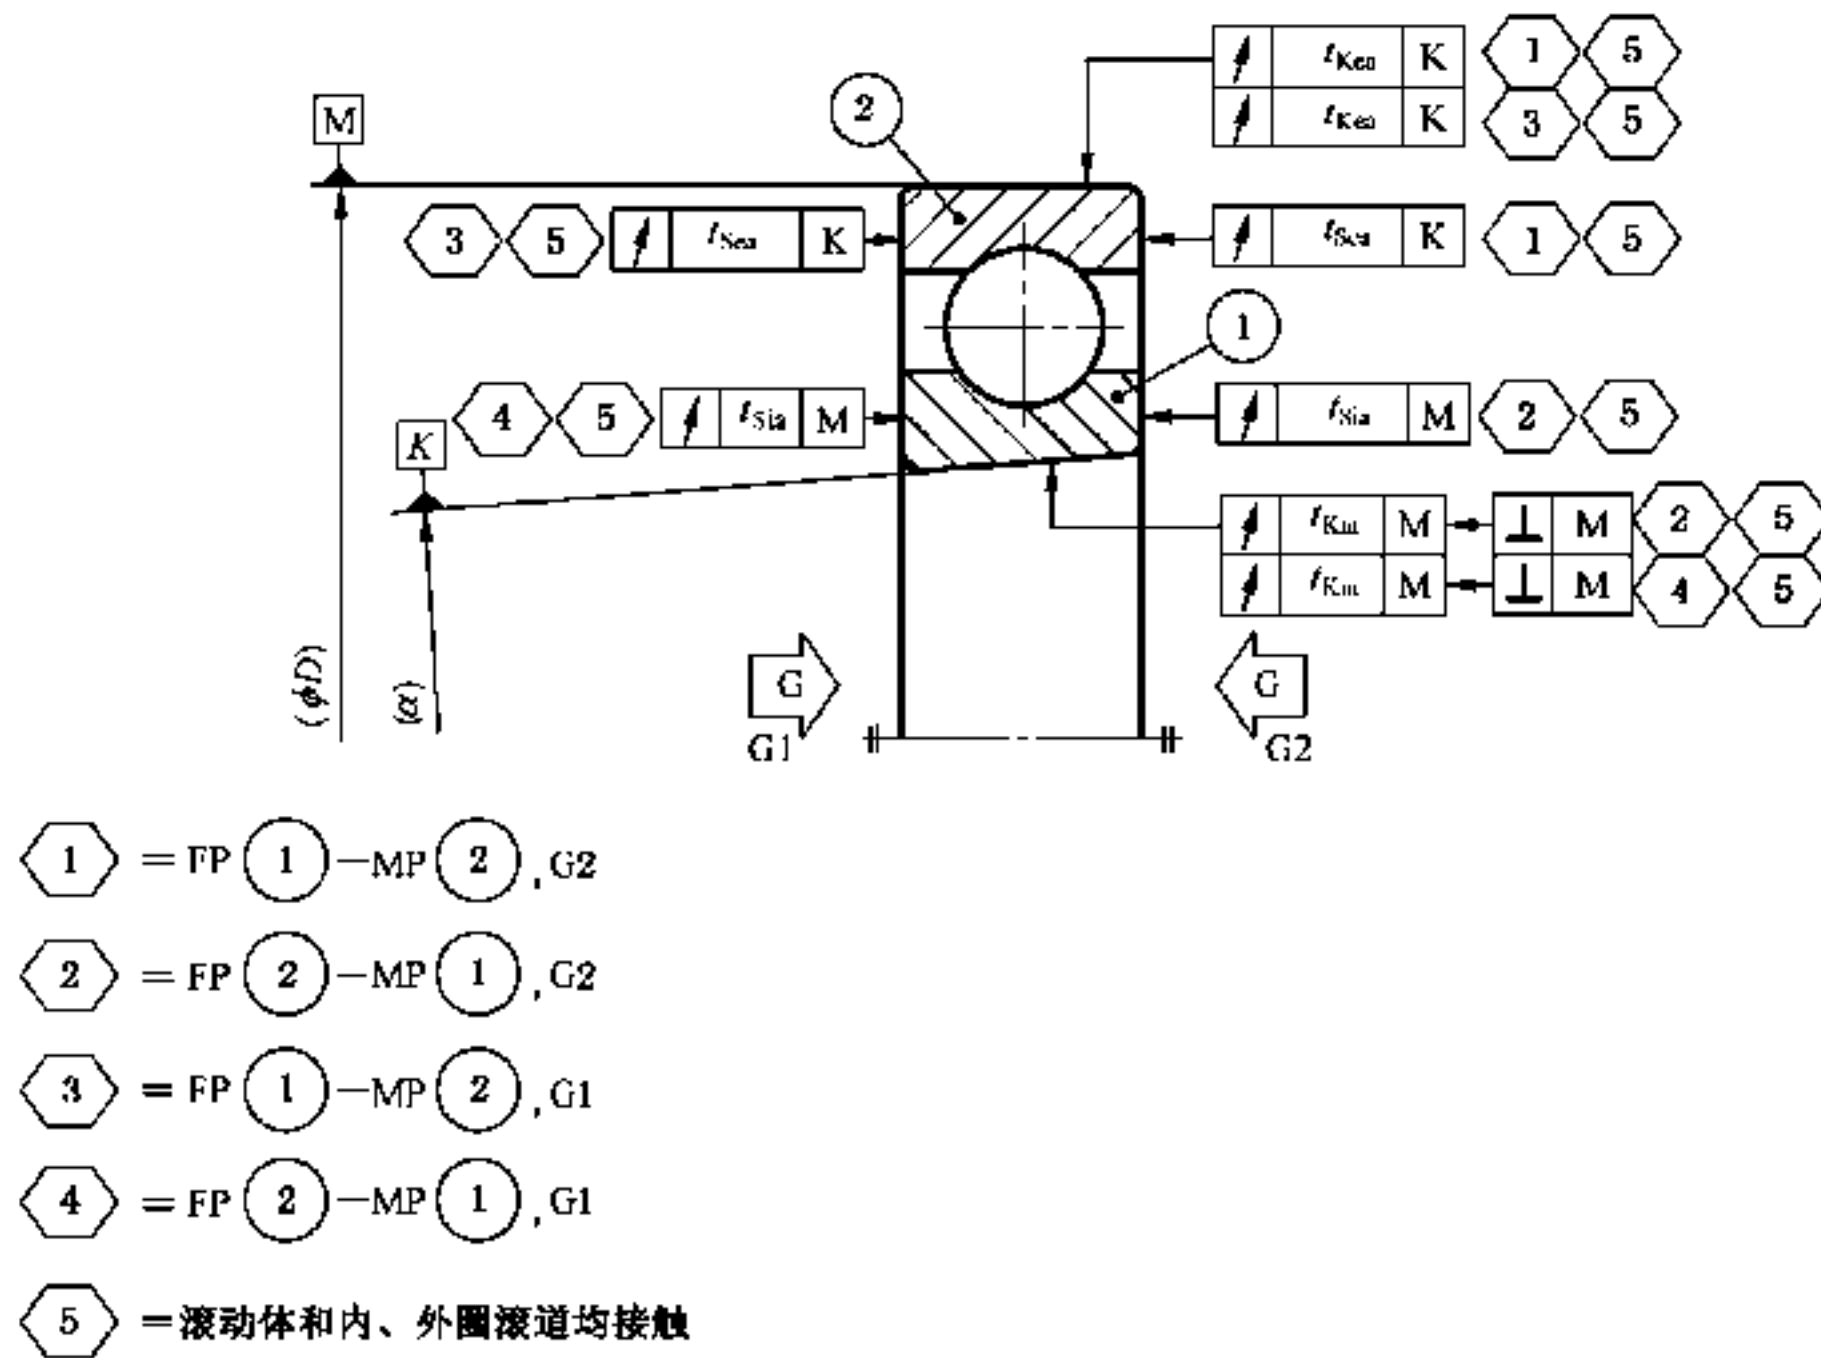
圆锥孔成套轴承的几何公差——深沟球轴承、双列深沟球轴承、双列角接触球轴承和四点接触球轴承
